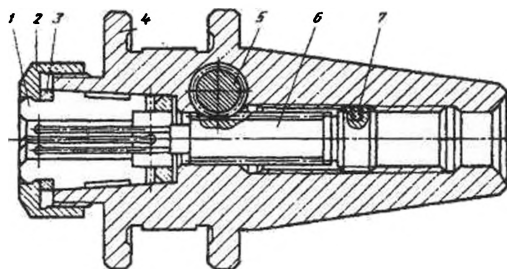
Патрон з механізмом регулювання вильоту інструмента
